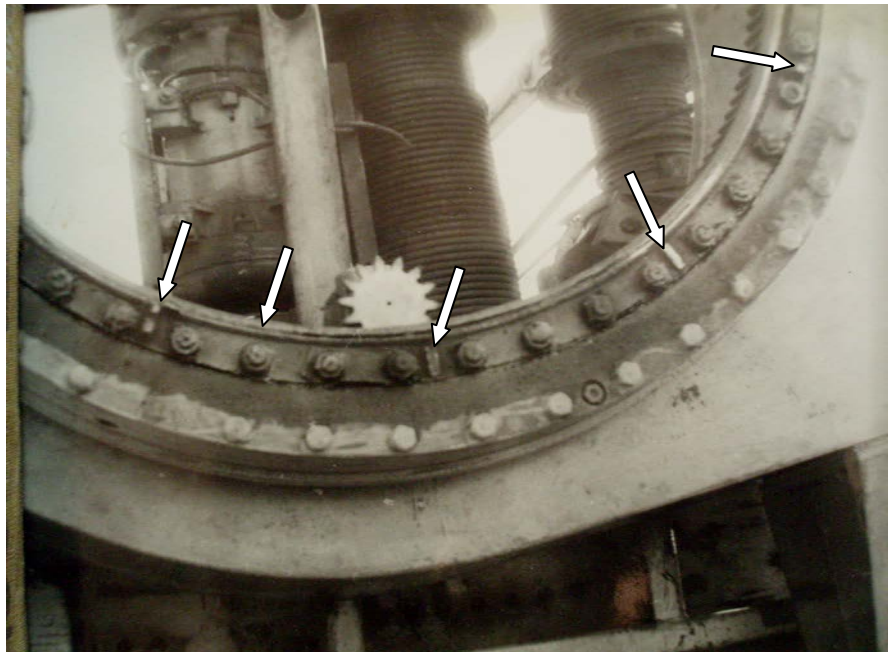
Фрагмент опорно-поворотного круга з дефектами (див. рис. 3), що спричинили обрив зварних швів металоконструкції неповоротної рами (вказані стрілками) і аварію баштового крана з перекиданням поворотної частини
